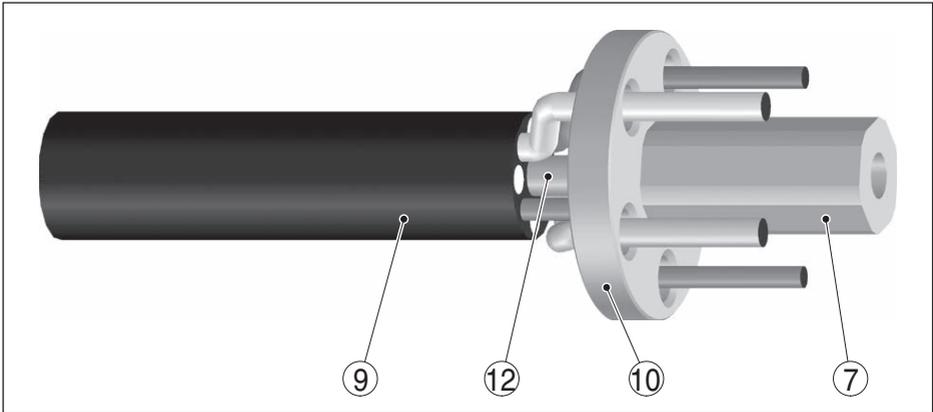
Cortar el cable de soporte (12) con el cortapernos
